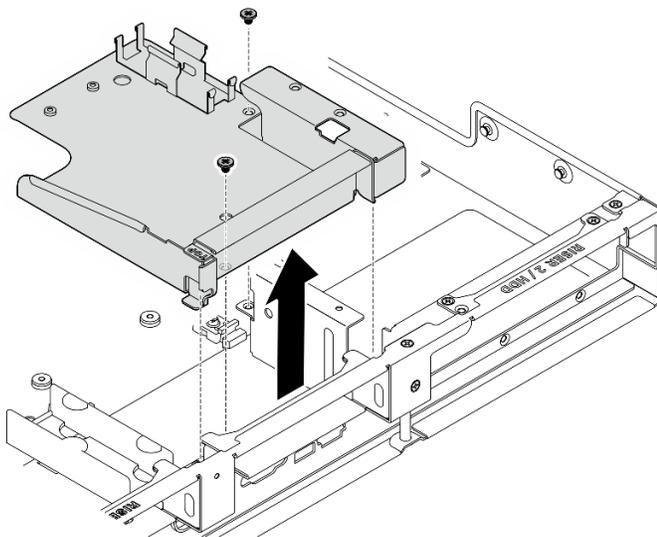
Removendo o suporte do módulo do sensor de vazamento
